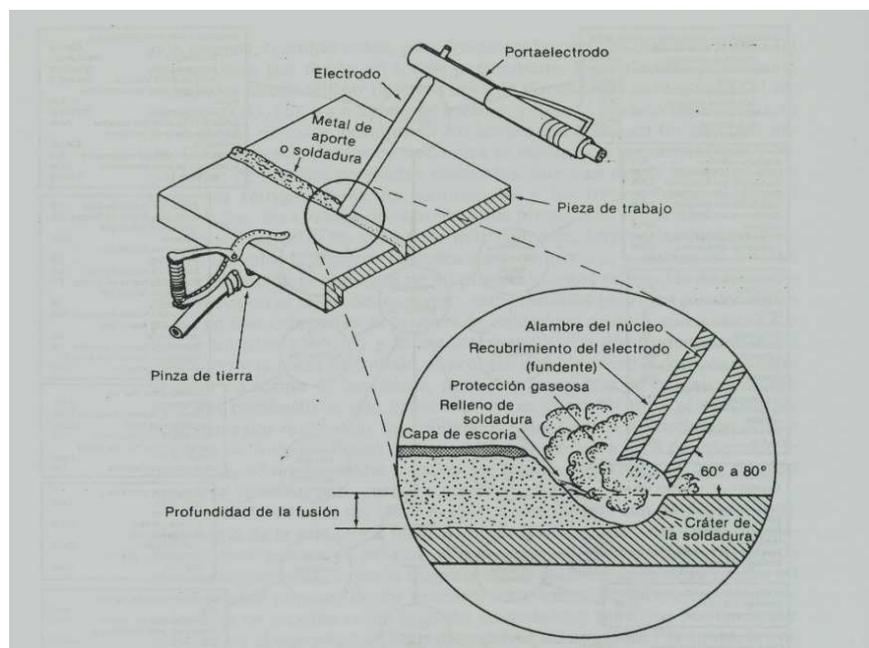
Soldadura de Arco<sup>3</sup>.
